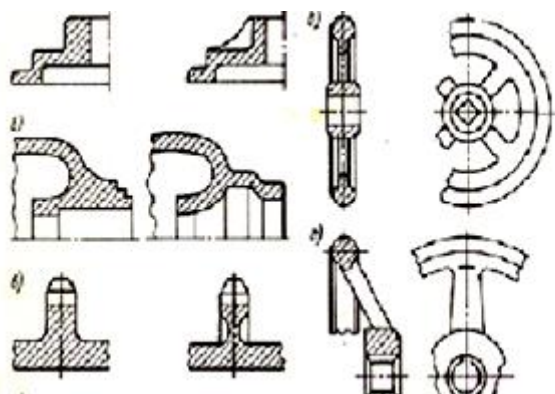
Конструктивные элементы деталей маховиков, шкивов, зубчатых колёс.
